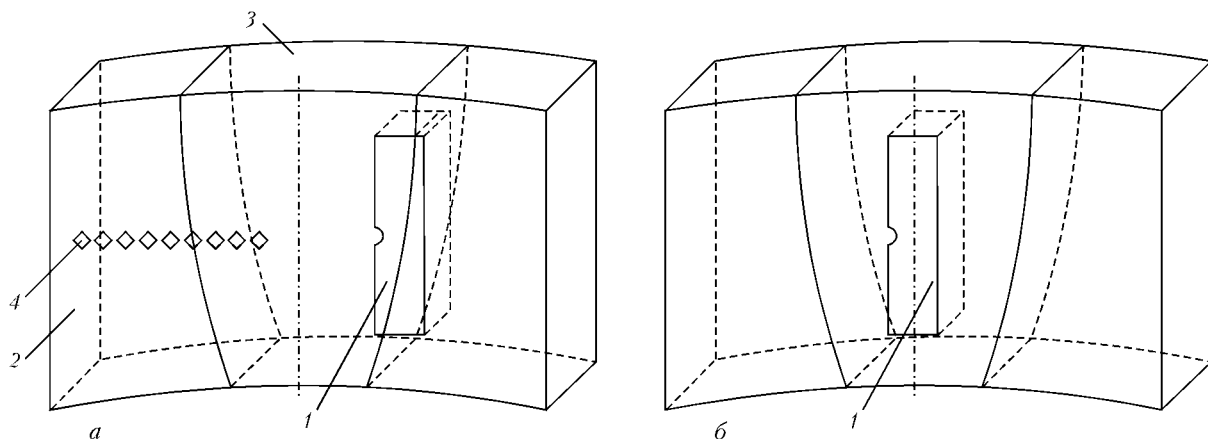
Схемы вырезки образцов для испытаний на ударный изгиб ( $KCU$ ) из металла сварного соединения паропровода участка сплавления (а) и металла шва (б): 1 — образец Менаже; 2 — основной металл; 3 — шов; 4 — места замеров микротвердости
